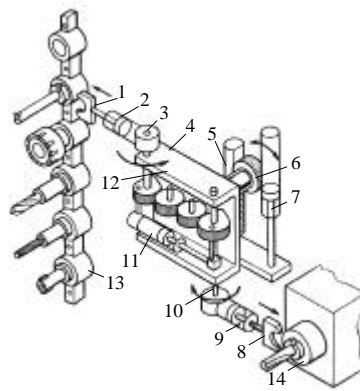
Дискретний механізм автоматичної заміни інструмента
